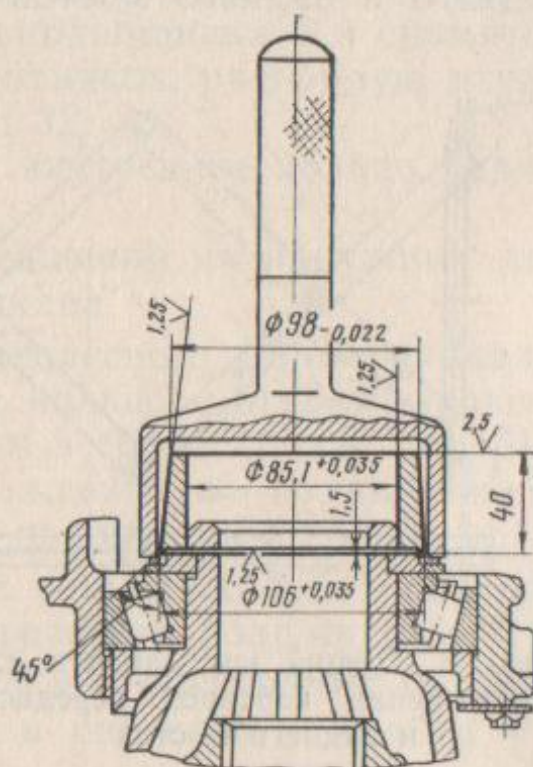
Оправка для установки кольца на сухарь подшипника чашки дифференциала
